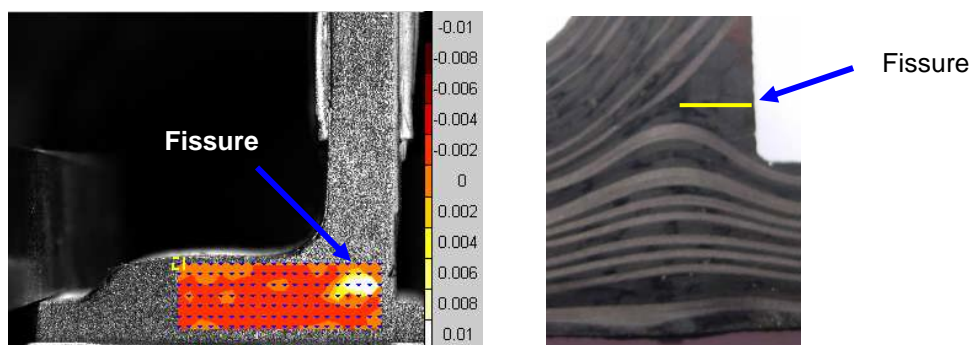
Déformations verticales sur la semelle, présence d'une fissure à l'interface à F=2800N (gauche) et position de la fissure sur l'éprouvette (droite).
